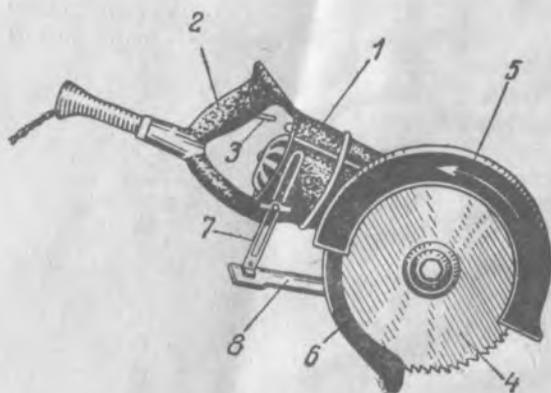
Редукторная электропила: 1 — электромотор, 2 — ручка, 3 — выключатель, 4 — пильный диск, 5 — верхний предохранительный кожух, 6 — нижний предохранительный кожух, 7 — регулирующее приспособление, 8 — опорная панель
